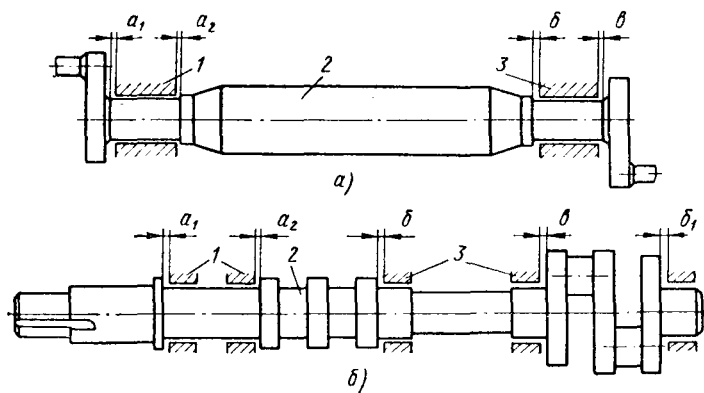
Схема проверки осевых зазоров в коренных подшипниках кривошипного (а) и коленчатого (б) вала:
